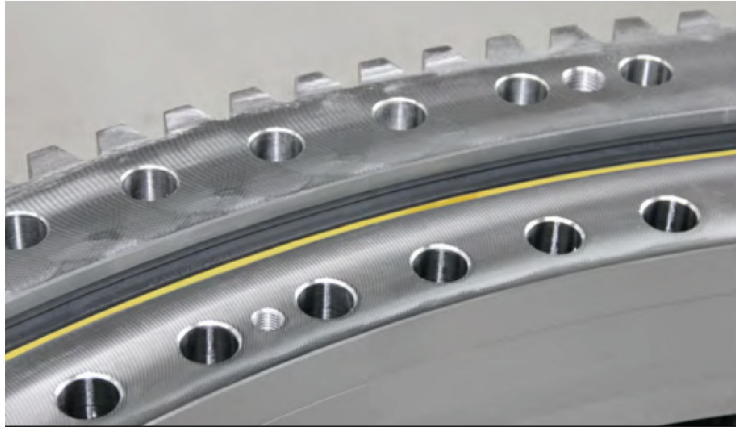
Geschlossener Fettkragen an Lagerdichtung
